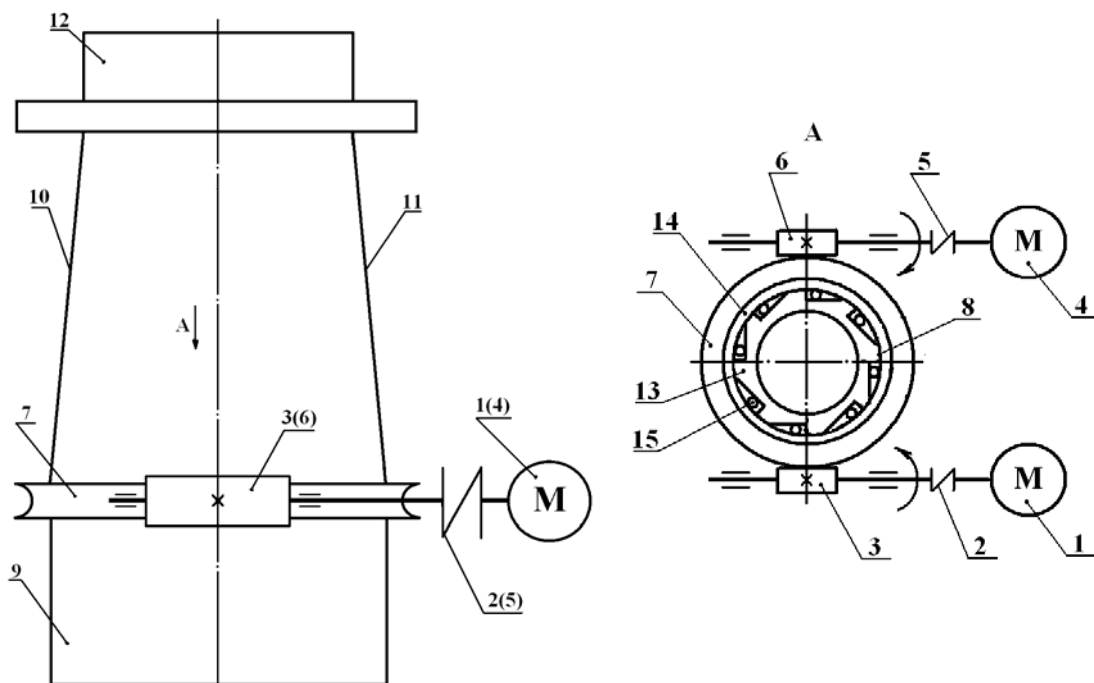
Кінематична схема двопоточного привода круглов'язальної машини з черв'ячними передачами
